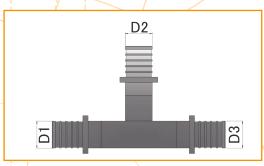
Пресс-тройник Тип 1 типоразмера 40
